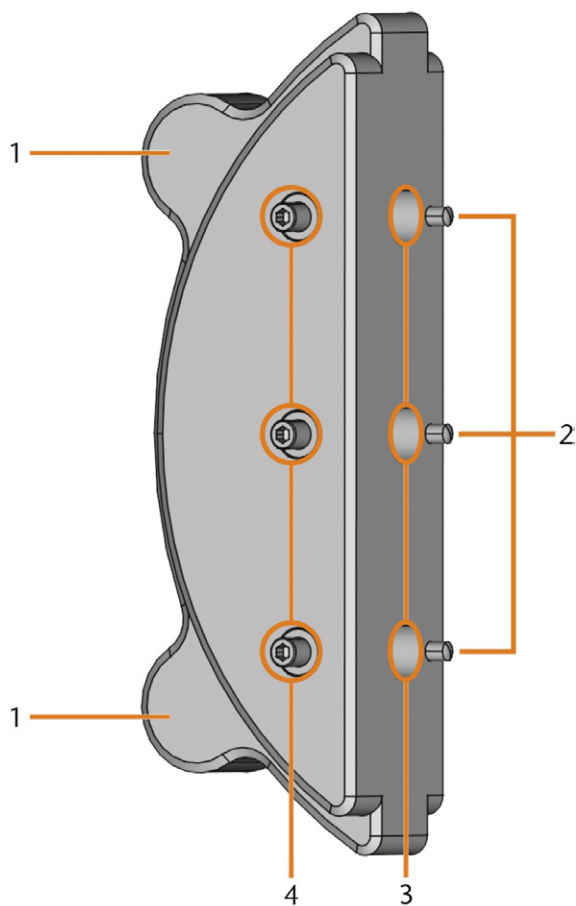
ДЕРЖАТЕЛЬ БЛОКА K5
